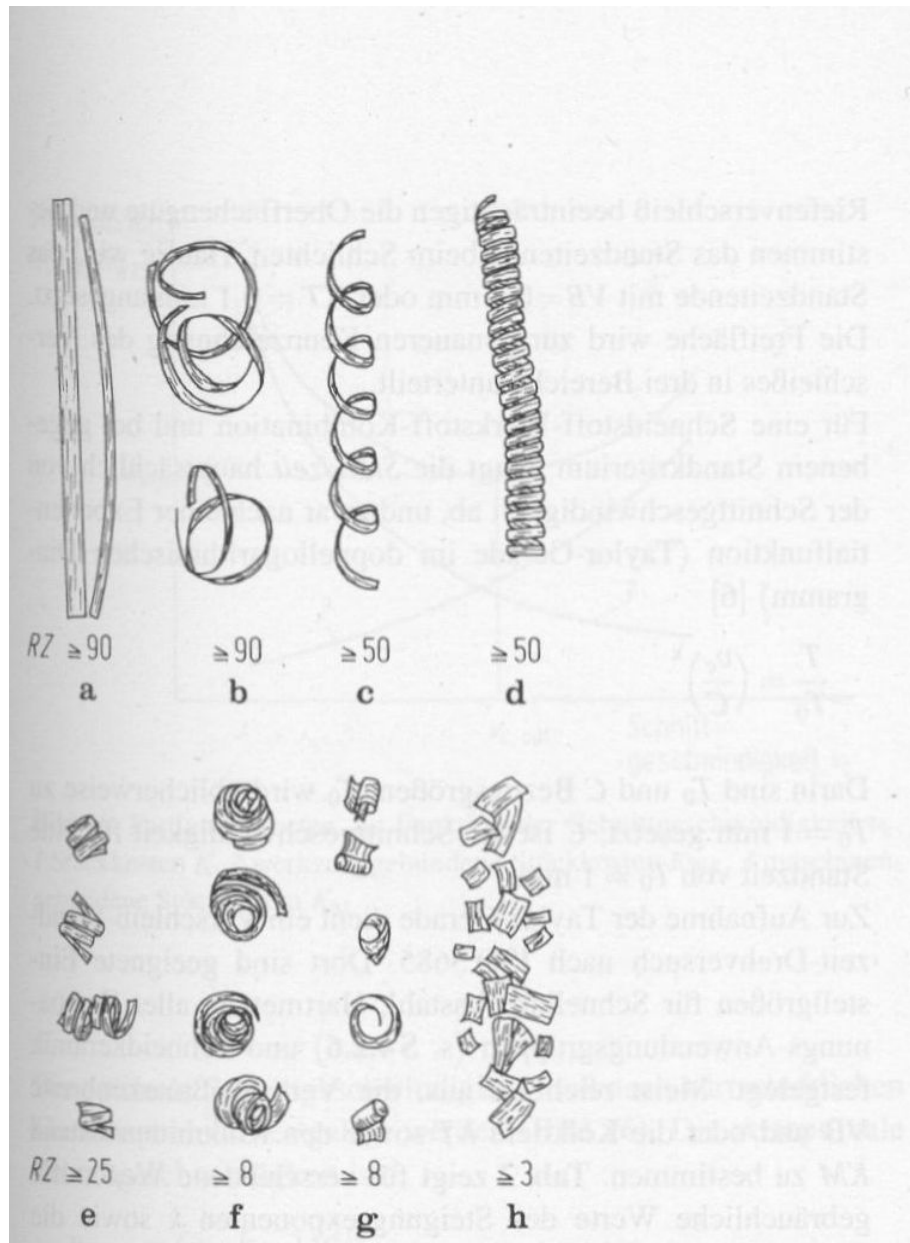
h. Spanformen (Stahl-Eisen-Prüfblatt 1178-69). a Bandspäne; B Wirrspäne; c Flachwendelspäne; d lange, zylindrische Wendelspäne; E Wendelspanstücke; f Spiralspäne; g Spiralspanstricke; h Bröckelspäne
